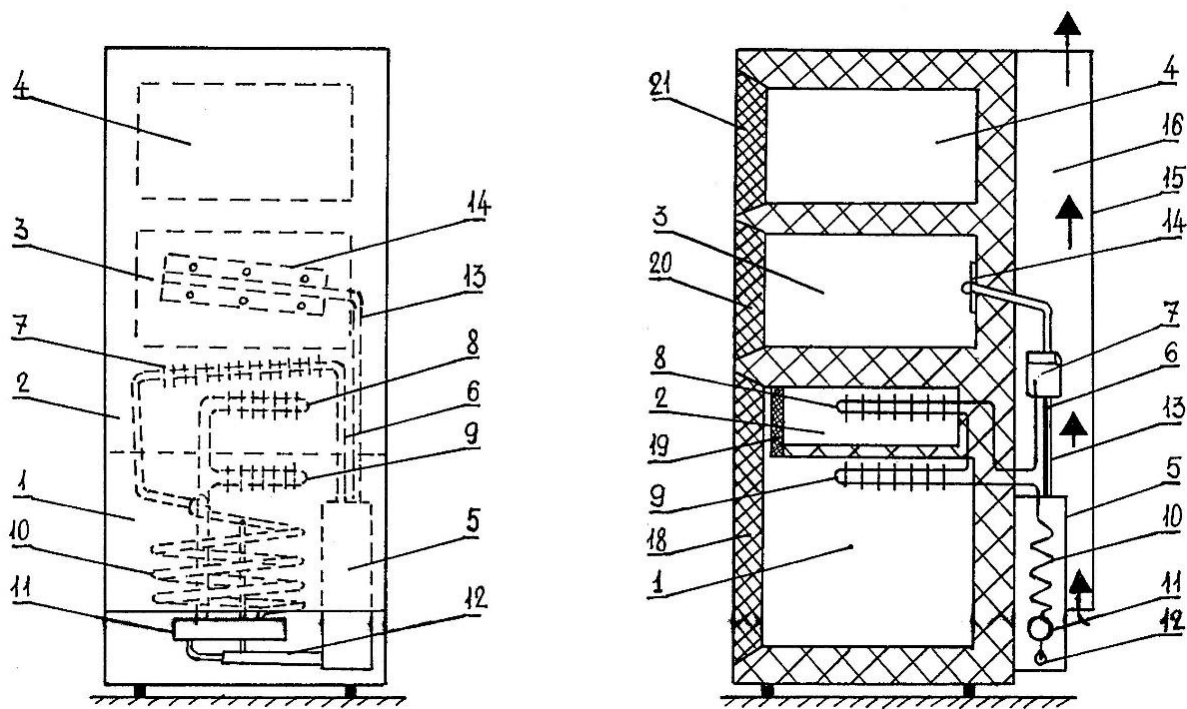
Конструкція комбінованого абсорбційного холодильного приладу із двома нагрівальними камерами: а) вид ззаду; б) вид збоку (розріз); 1 – ХК; 2 – НТВ; 3 – нагрівальна камера; 4 – камера підігріву; 5 – генераторний вузол; 6 – дефлегматор; 7 – конденсатор; 8, 9 – випарники; 10 – абсорбер; 11 – бачок абсорбера; 12 – рідинний теплообмінник; 13 – ДФТС; 14 – конденсатор ДФТС; 15 – витяжний кожух; 16 – витяжна порожнина; 18-21 – теплоізовані двері камер
